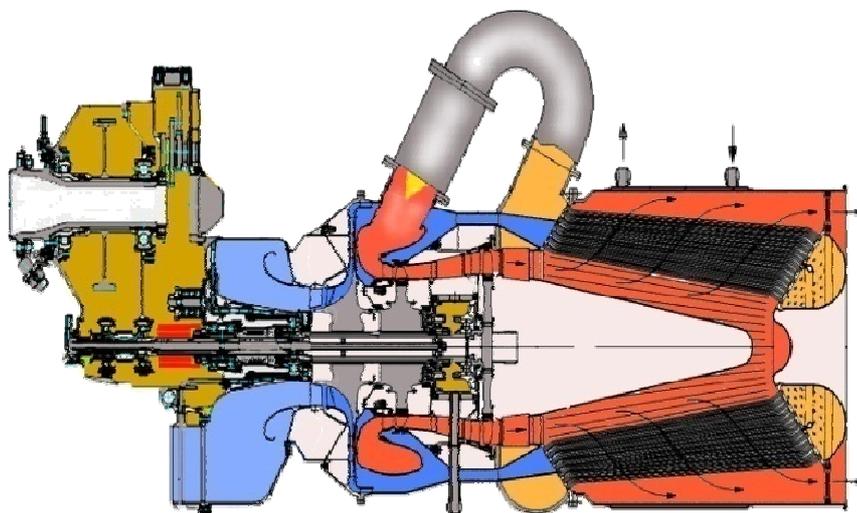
Конструктивная схема двигателя НК-123 с встроенным рекуператором
